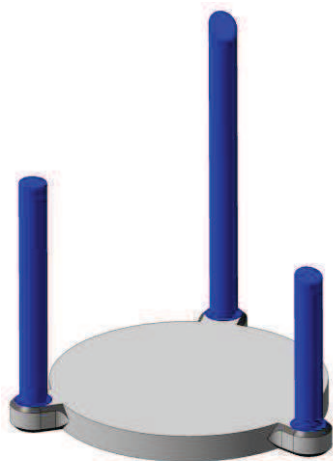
3D модель диска с консольным креплением направляющих опор.
